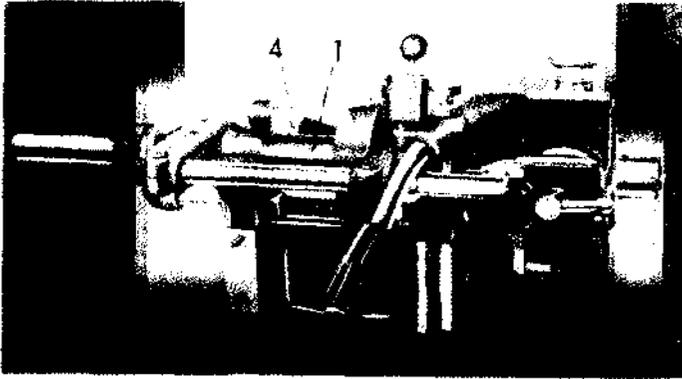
Dispositivo para roscar con patrón. — 1, Patrón. — 2, Herramienta. — 3, Palanca para poner en contacto el palpador sobre el patrón. — 4, Palpador.
